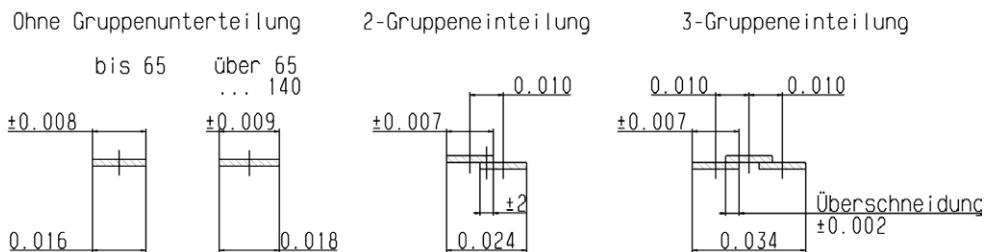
Kolbenform, Maß- und Formtoleranzen
